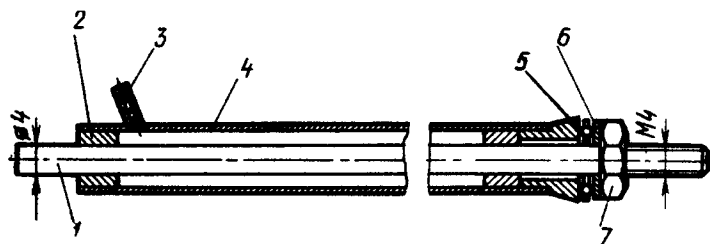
Дейдвудная труба с упорным шариковым подшипником со стороны двигателя:
